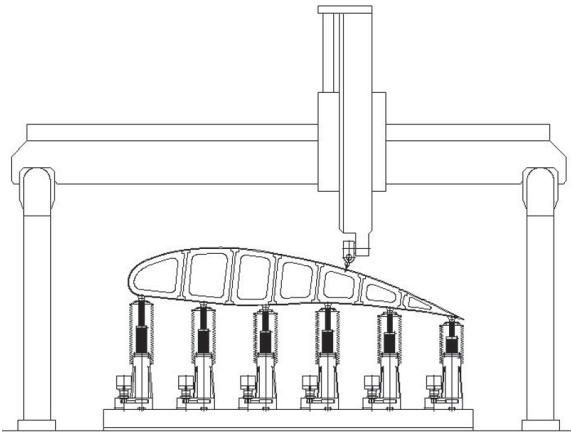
Aufspannen und Ausrichten mit Teleskop-Kugelgewindetrieben.
